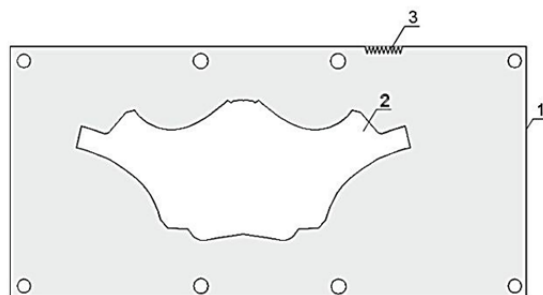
Заготовка технологической оснастки для деталей верха самого большого размера
